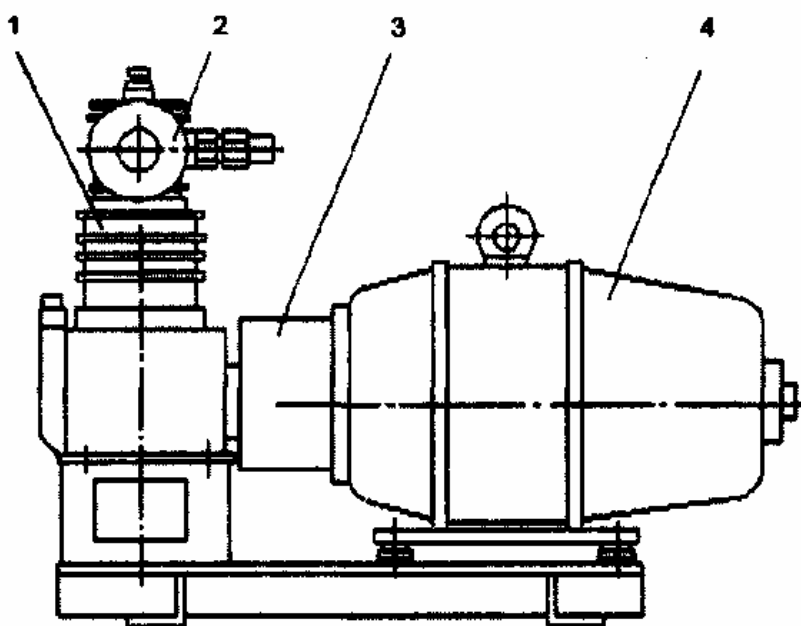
Компрессор ВВ 0,05/7-1000 1 - компрессор; 2 - фильтр воздушный; 3 - ограждение муфты; 4 – электродвигатель
